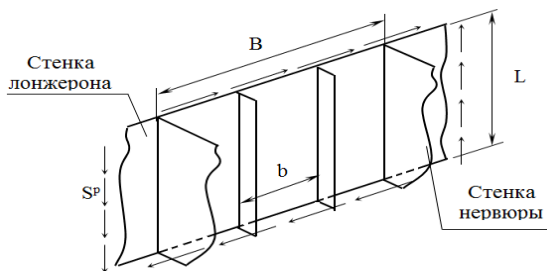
Фрагмент подкрепленной стенки лонжерона
